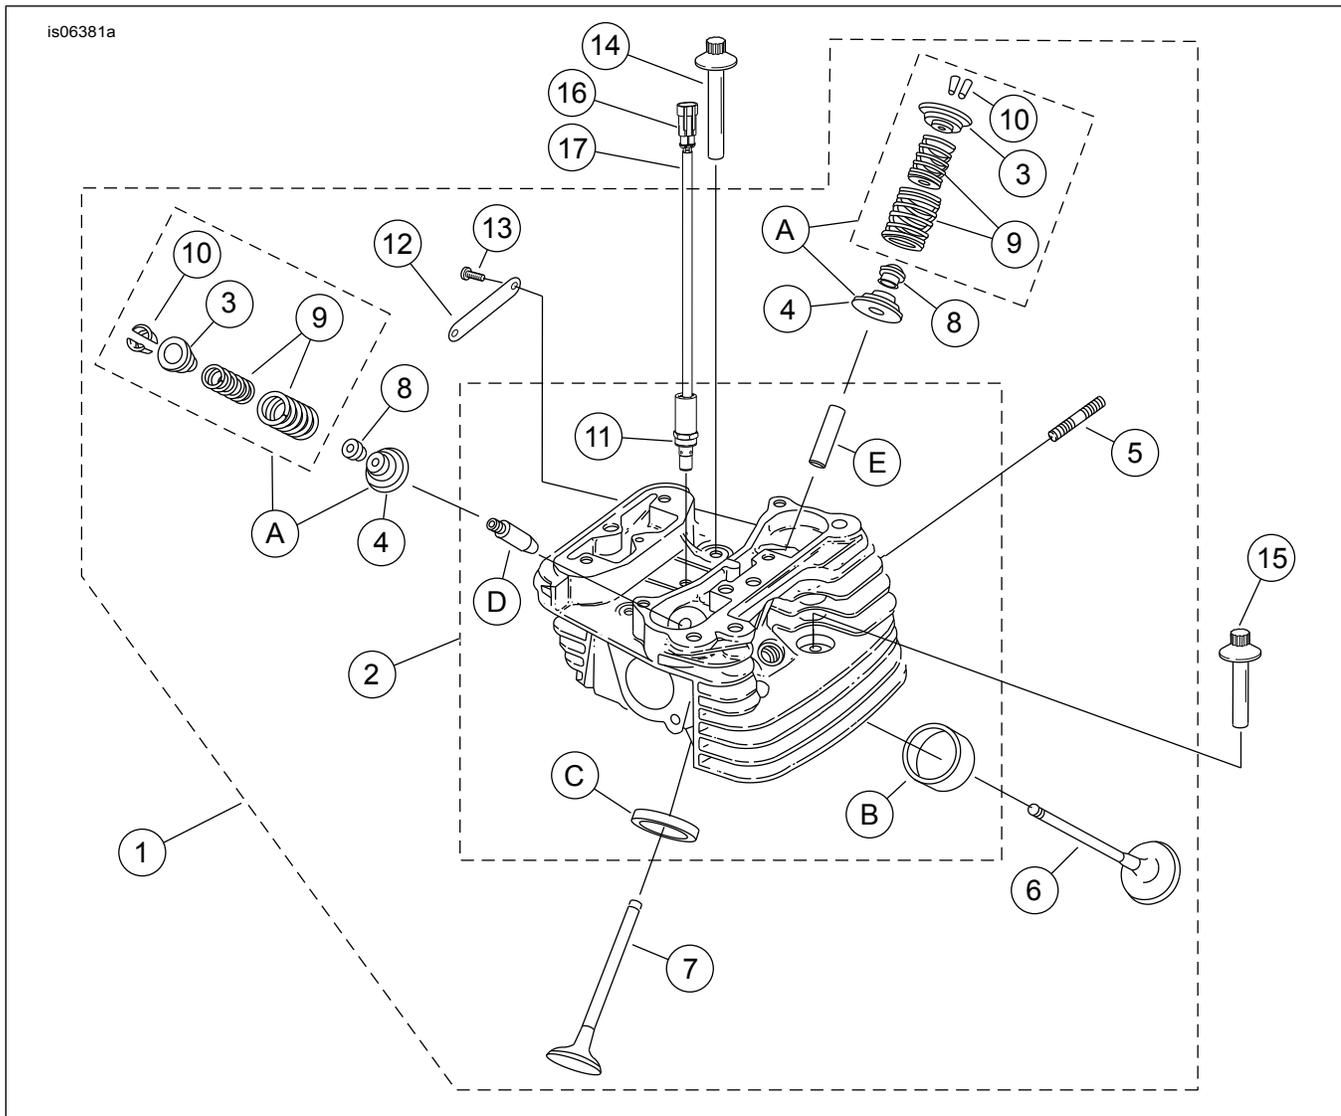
Culatas de los cilindros y válvulas del motor ensamblado Screamin' Eagle Pro SE120R (Beta)
